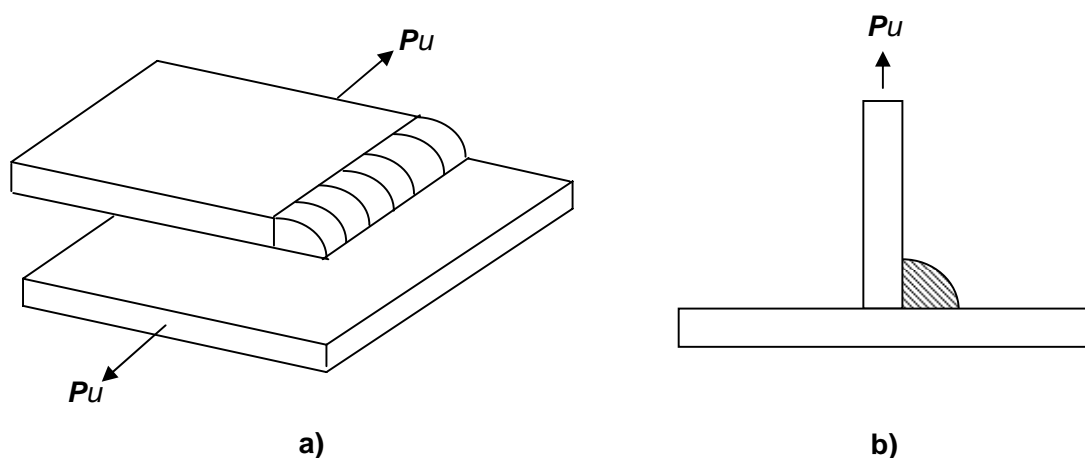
a) Esquema de los esfuerzos en soldadura de filete longitudinal b) Soldadura de filete transversal ^[9].
